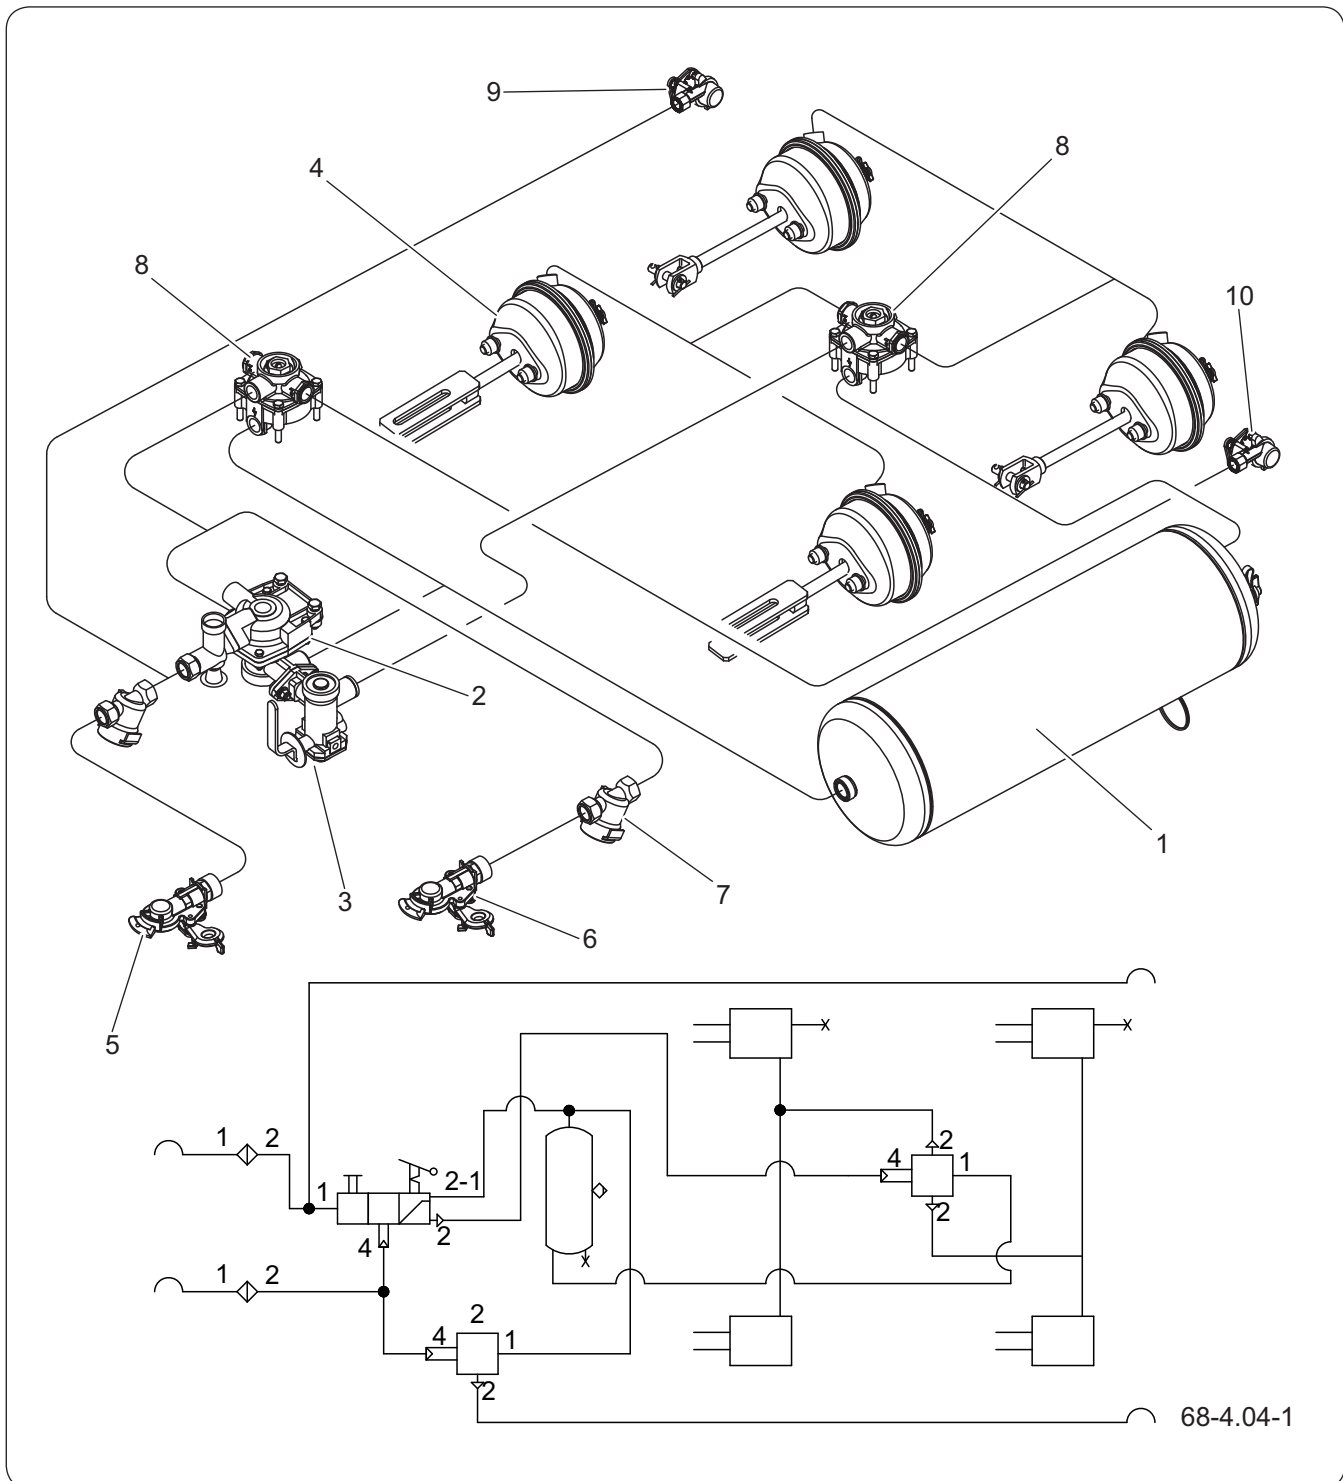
Aufbau und Schema der Zweileitungs-Druckluftbremsanlage mit manuellem Bremskraftregler.
